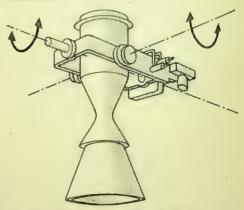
Kardanisch gelagertes Hilfstriebwerk zur Lagesteuerung
